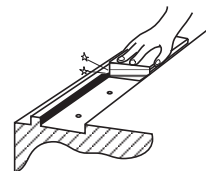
Montage bei hohen Bearbeitungskräften durch unterbrochenen Schnitt. Montage bei THK-Führungen z.B. mit Andruckschrauben.
